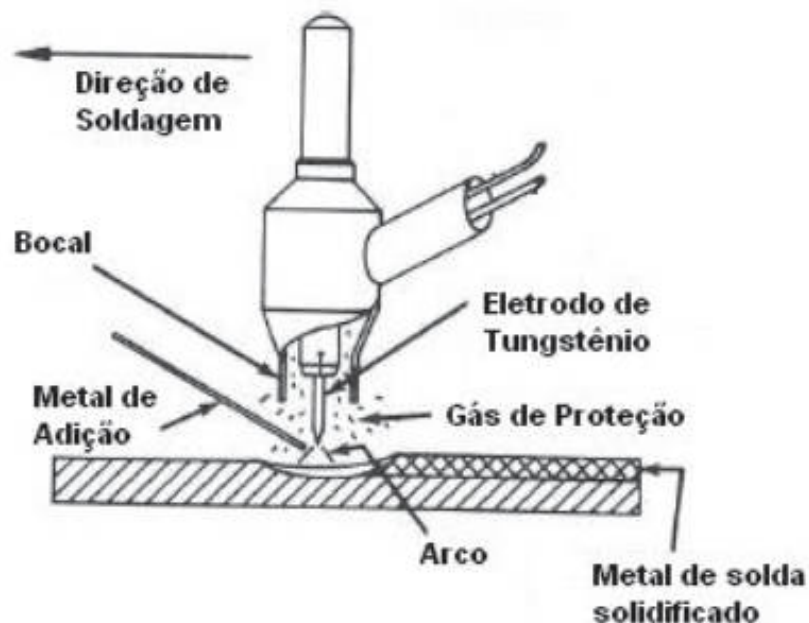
Soldagem TIG esquemática (Cantarini, 2011)
